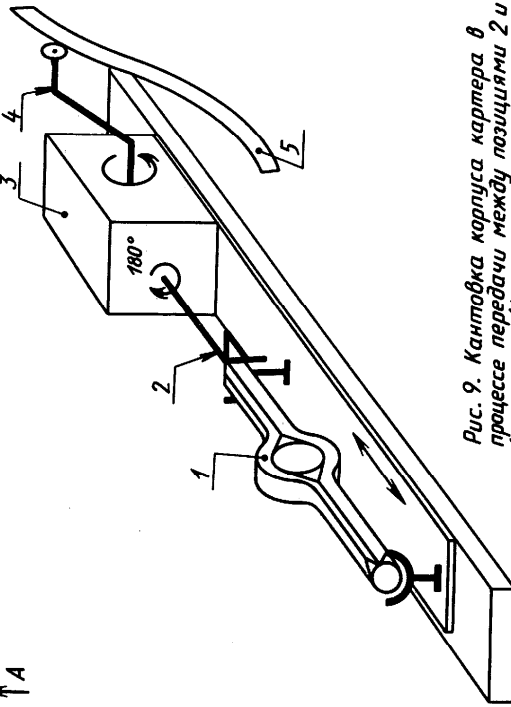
Кантовка корпуса картера в процессе передачи между позициями 2 и 3 (см. рис. 3 и 4)
